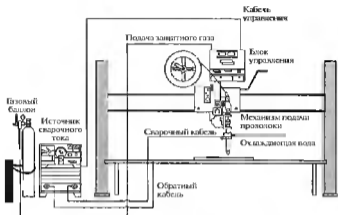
Установка для автоматической сварки в защитном газе
